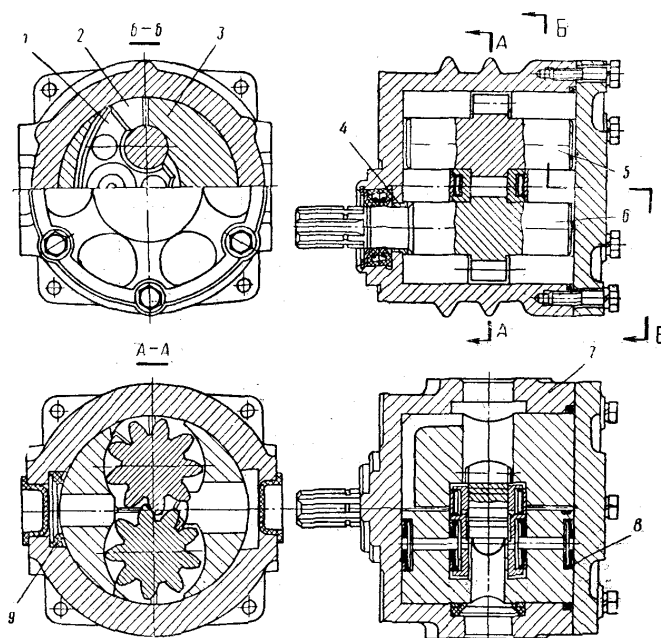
Шестеренный насос типа НШ-100 (круглый): 1- пластик; 2 – поджимная обойма; 3 – обойма-подшипник; 4 - втулка; 5, 6 – вал-шестерни; 7- корпус; 8, 9- манжеты.
